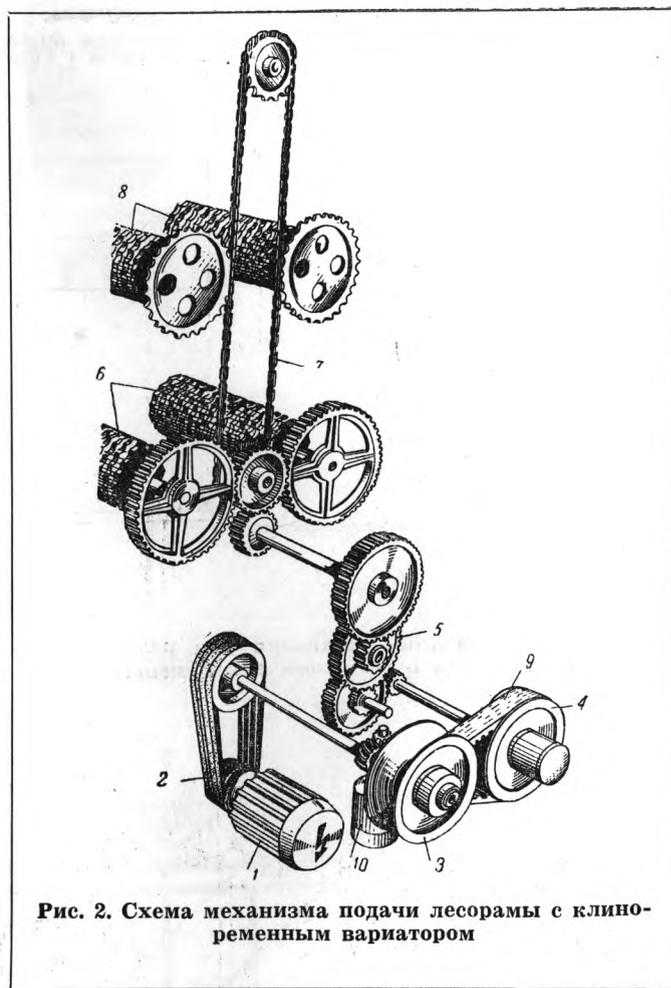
Схема механизма подачи лесорама с клиноремennым вариатором
